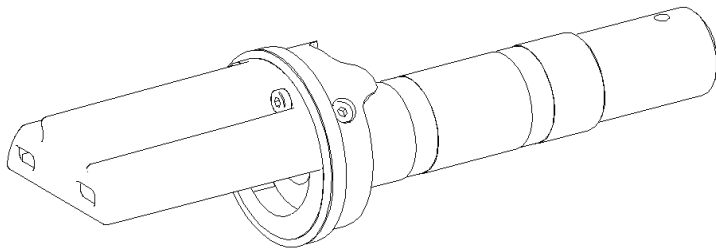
Cella di carico a grillo – Perno estensimetrato e scheda elettronica
